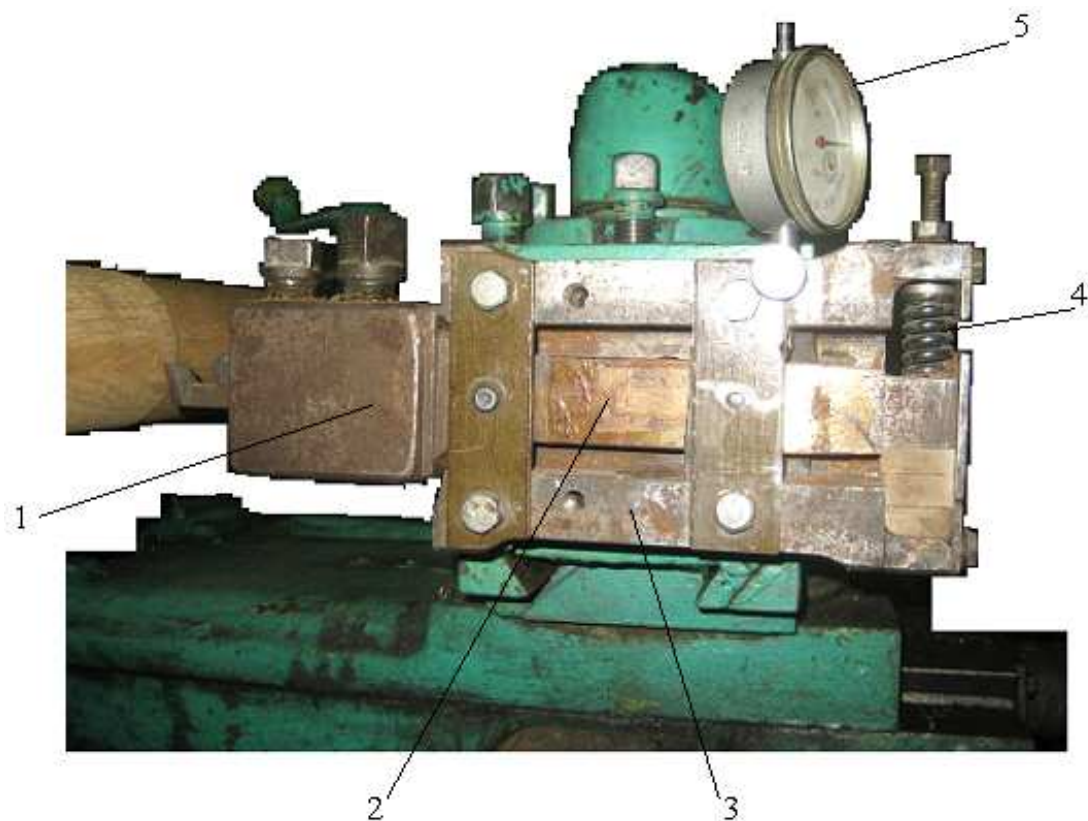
1 – люлька; 2 – рычажная планка; 3 – корпус; 4 – пружина; 5 – индикатор
